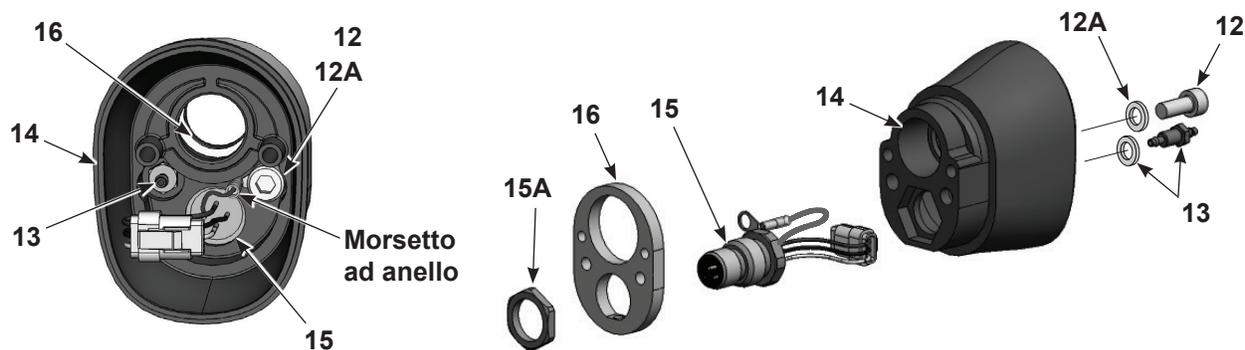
Smontaggio della pistola a spruzzo con montaggio su tubo 5 di 5
